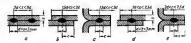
Dimensiones de las costuras por puntos y por contacto de redillo
